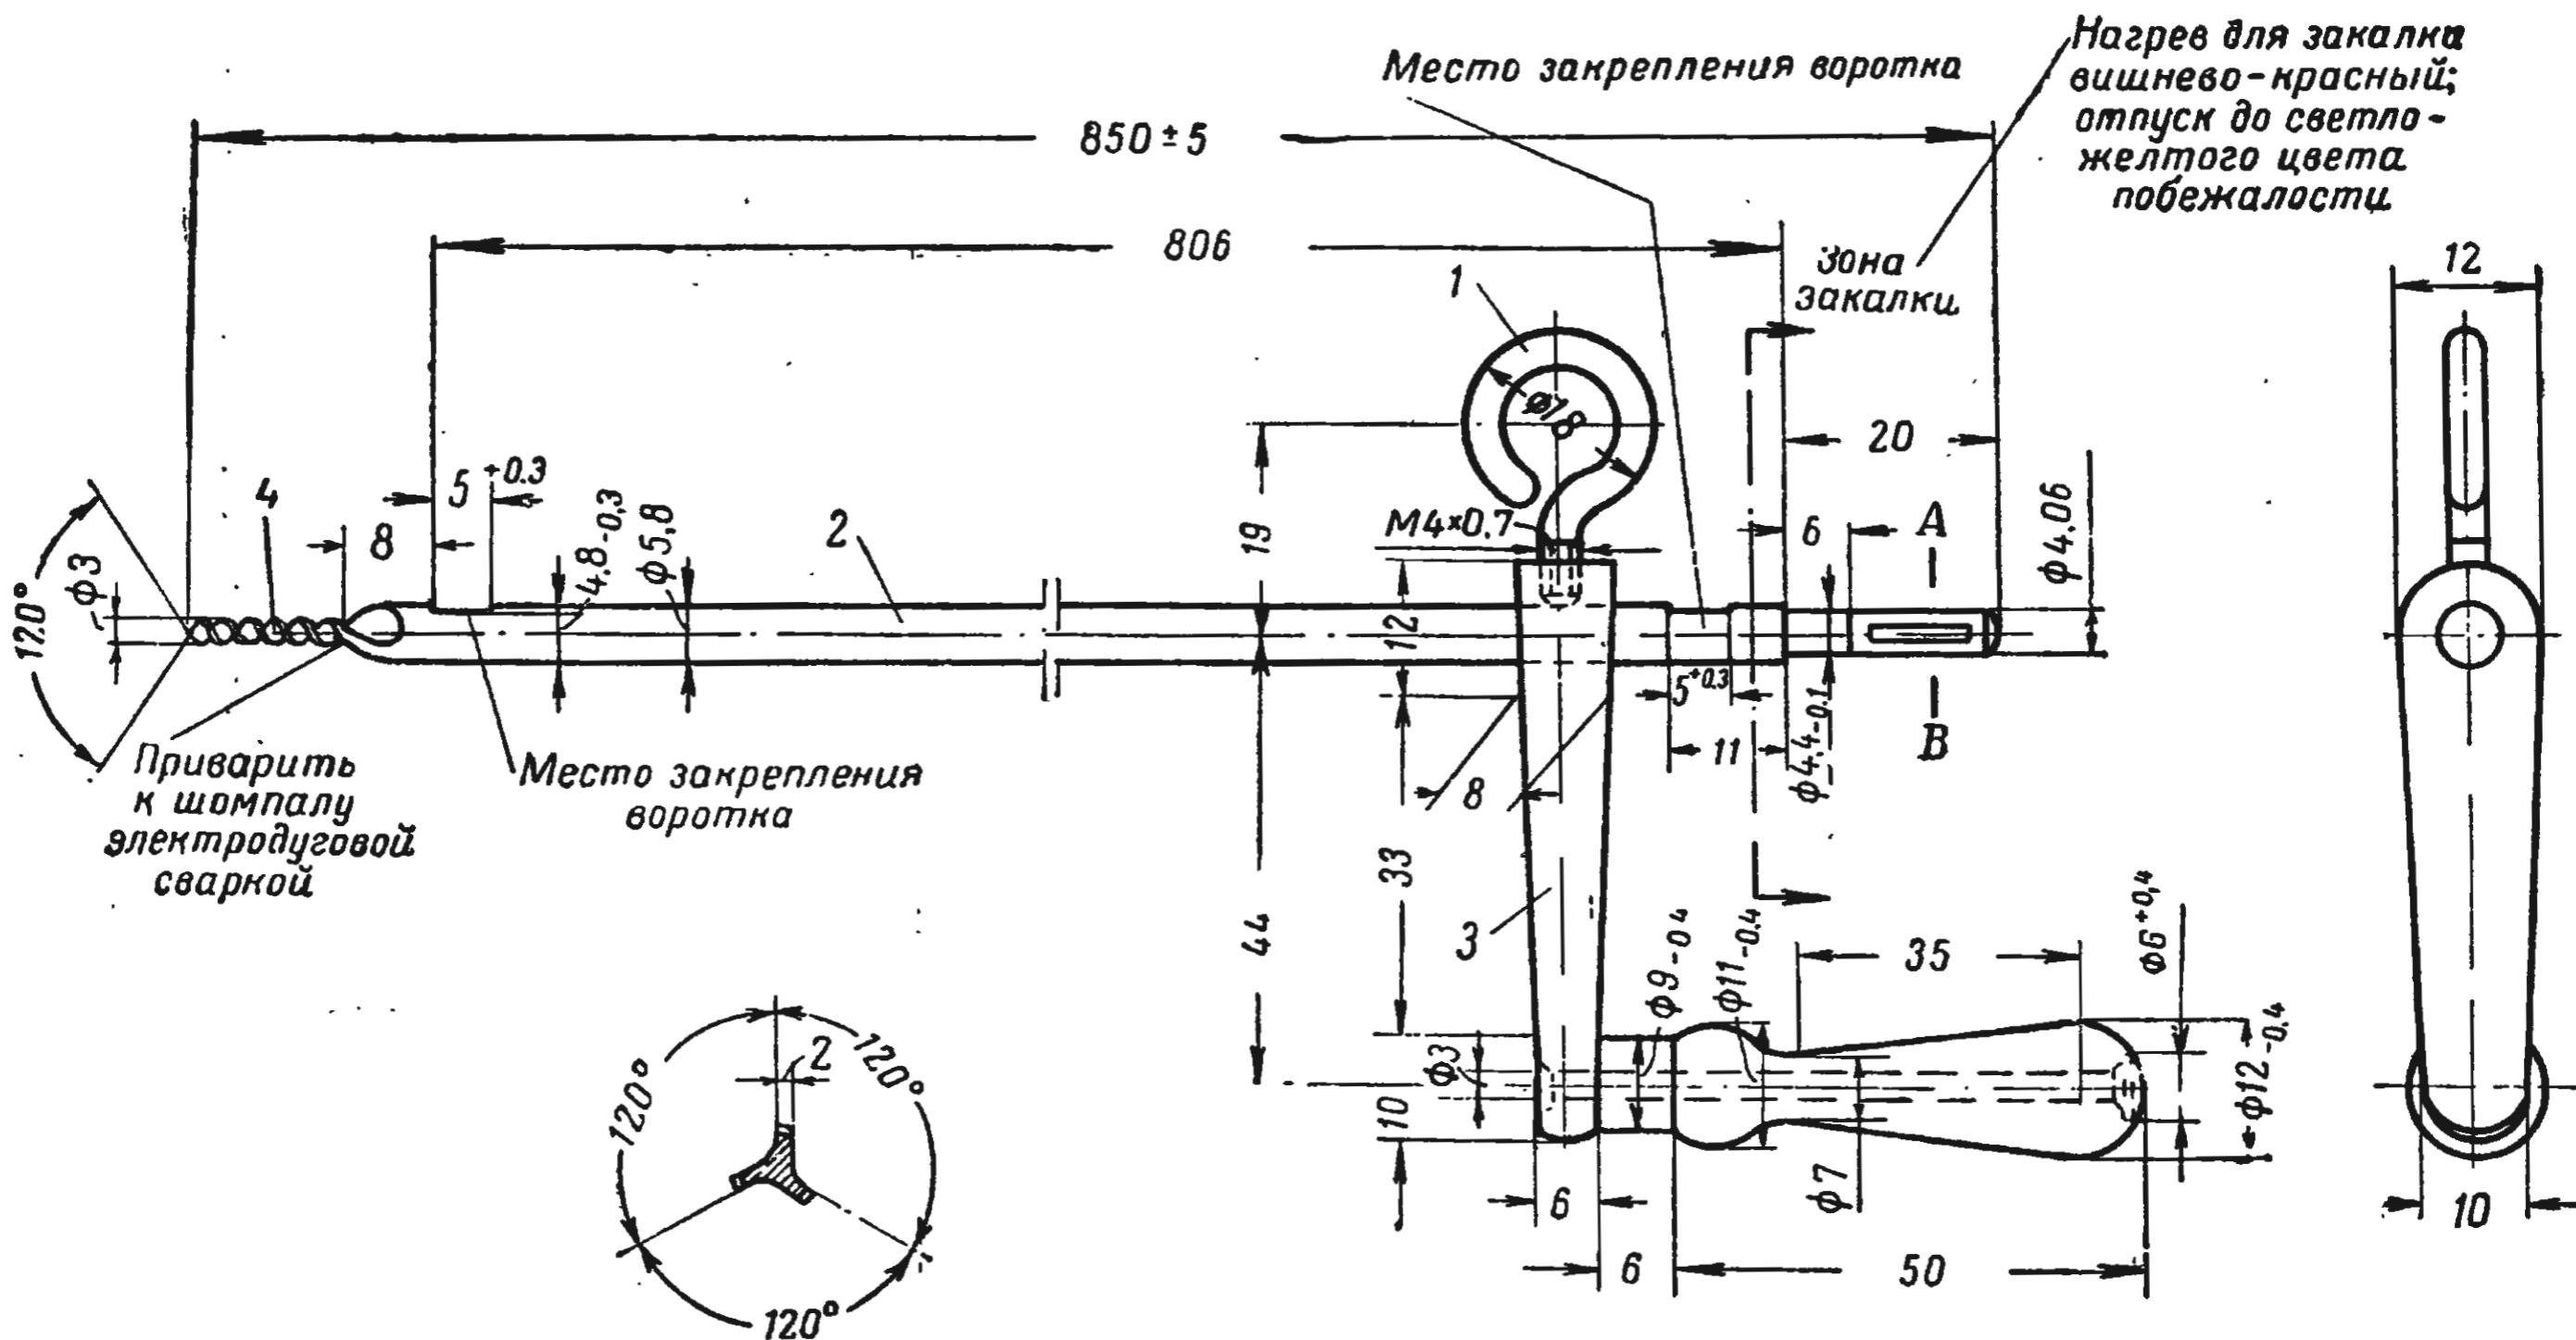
Прибор для прочистки нарезного отверстия шомпольного упора:
